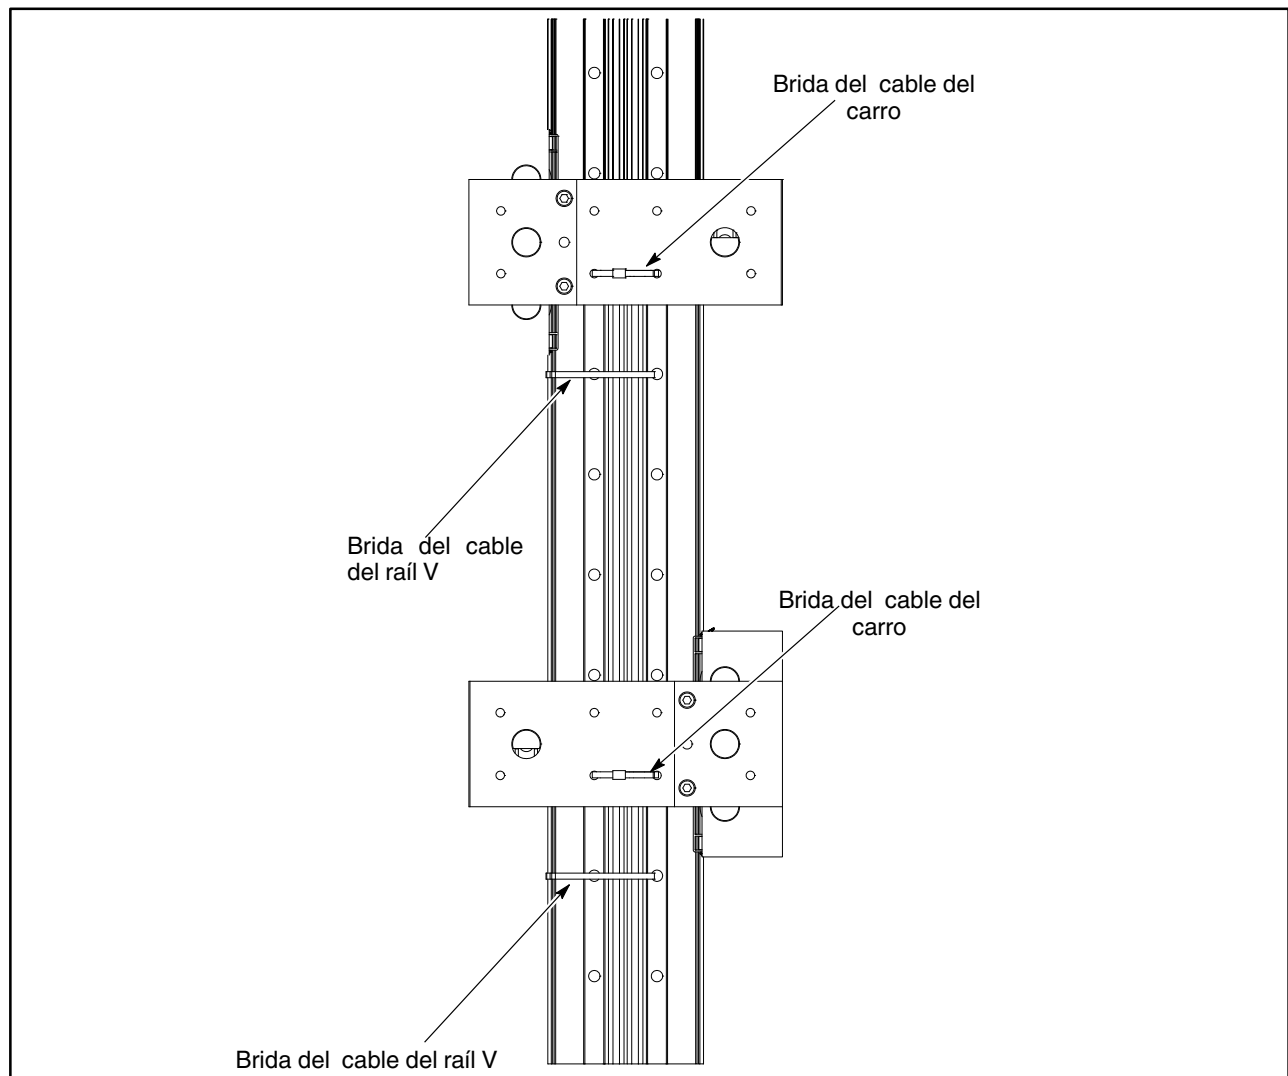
Extracción de las bridas del cable desde el conjunto del carro
